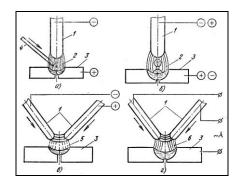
Схемы электродуговой сварки (1 — электрод; 2 — дуга прямого действия; 3 — основной металл; 4 — присадочный металл; 5 — дуга косвенного действия; 6 — трёхфазная дуга): а) неплавящимся электродом; б) плавящимся электродом; в) косвенной дугой; г) трёхфазной дугой.
